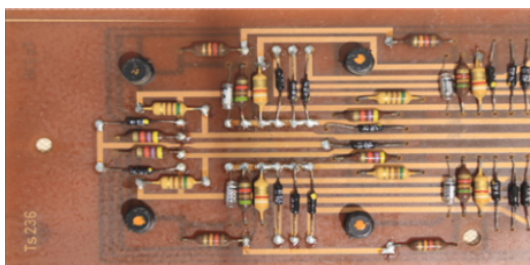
Deska plošných / tištěných spojů (PCB)
